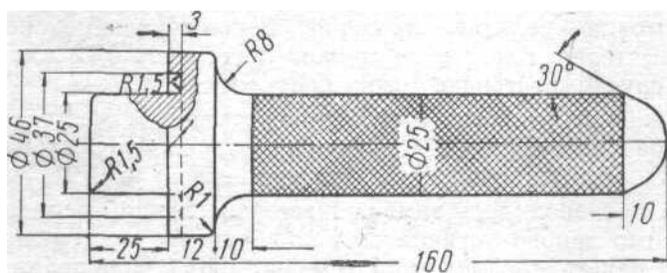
Оправка для напрессовывания подшипников коробки дифференциала
